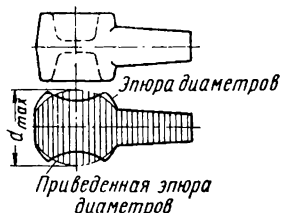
Способ приведения расчетной заготовки с резким очертанием к плавной форме
